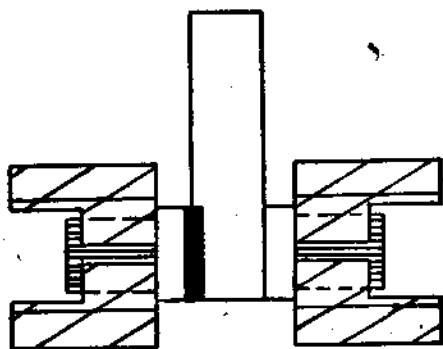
Подготовка для сварки встык брусков неодинакового сечения.
